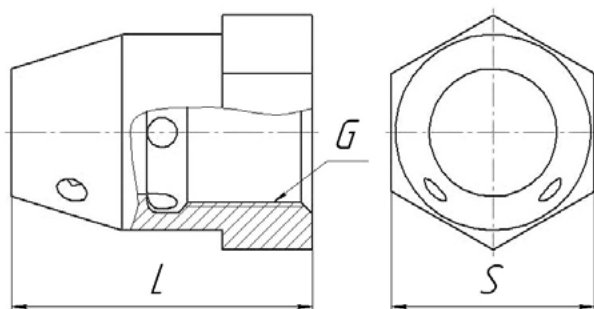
Насадки (сопла) угловые с внутренней резьбой
